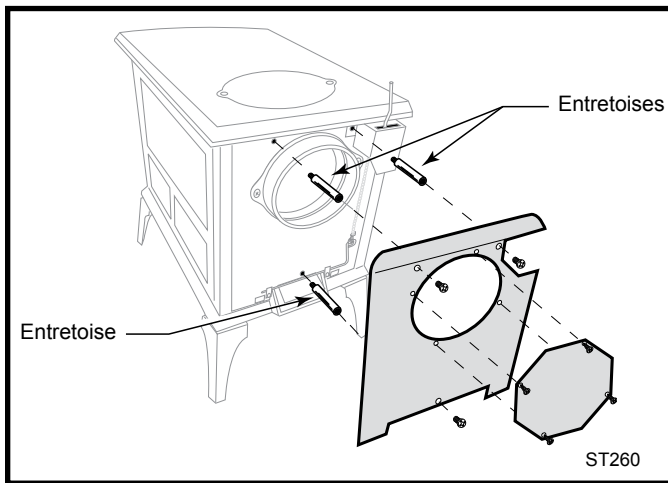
Assemblage de l'écran pare-chaleur arrière.
